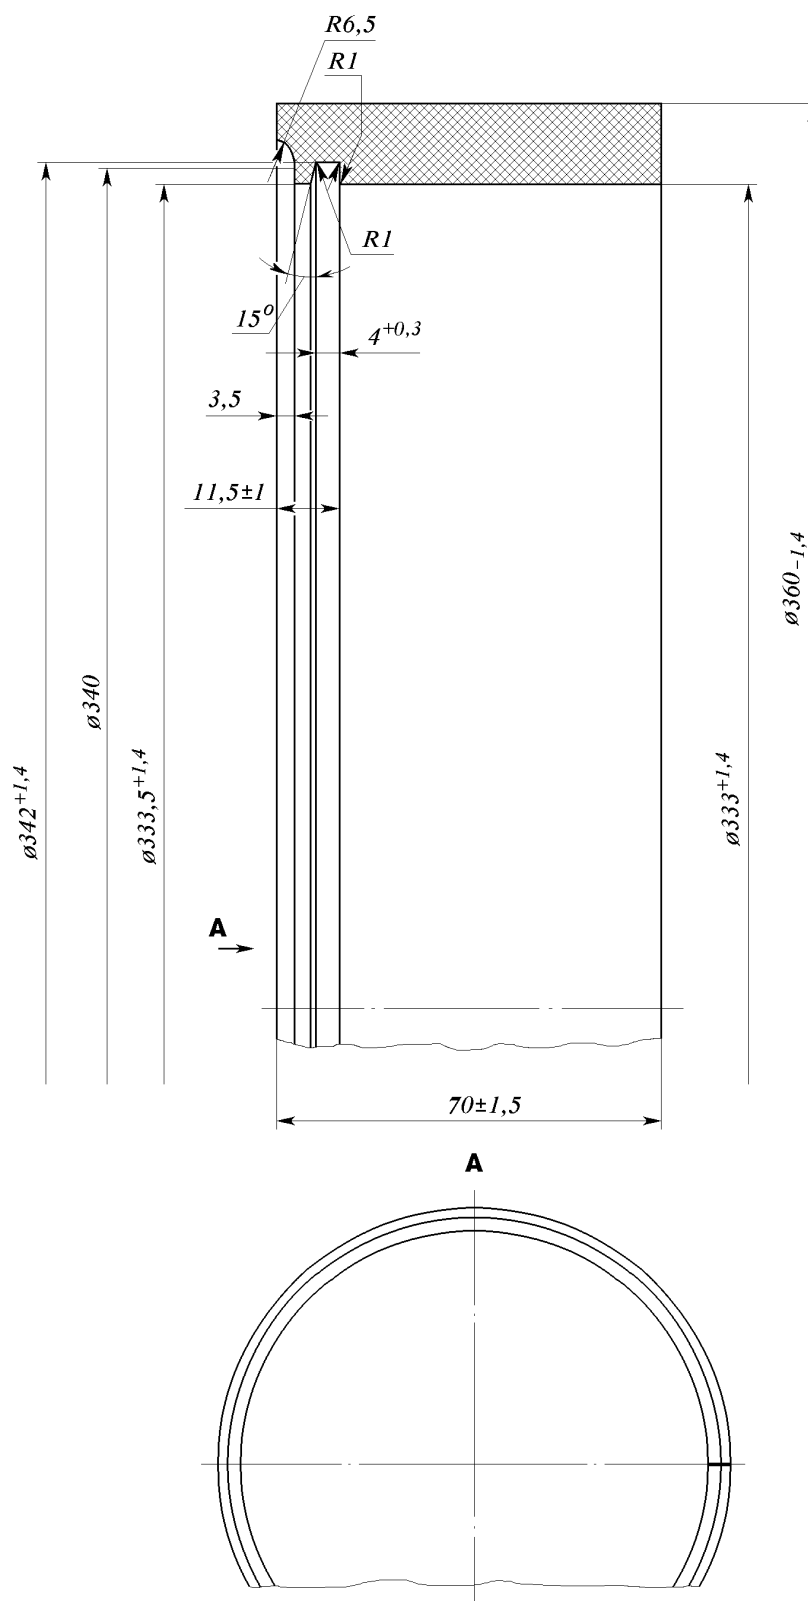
Кольцо монтажное для установки торцового уплотнения (76.90Н-28А4 HN60)
